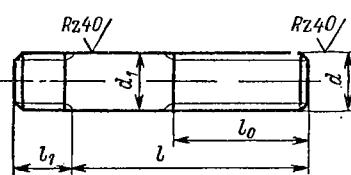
Шпильки общего применения повышенной точности для деталей с резьбовыми отверстиями
